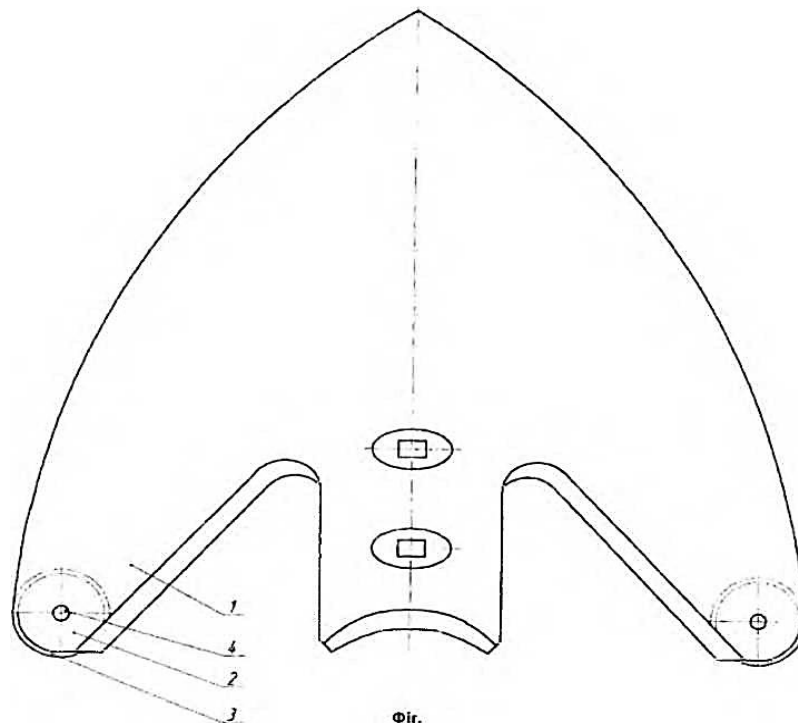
Робочий орган культиватора [16], вид зверху
